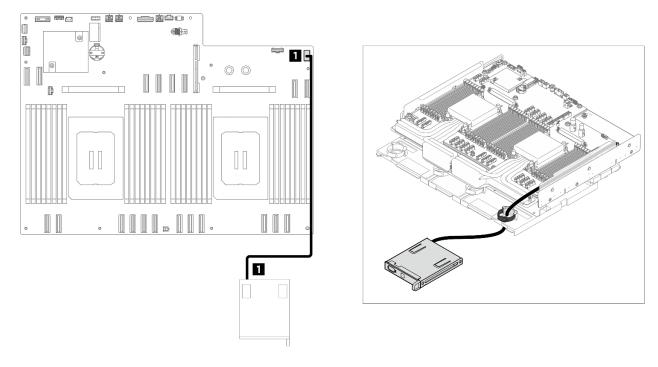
Disposición de los cables del panel de diagnóstico integrado
